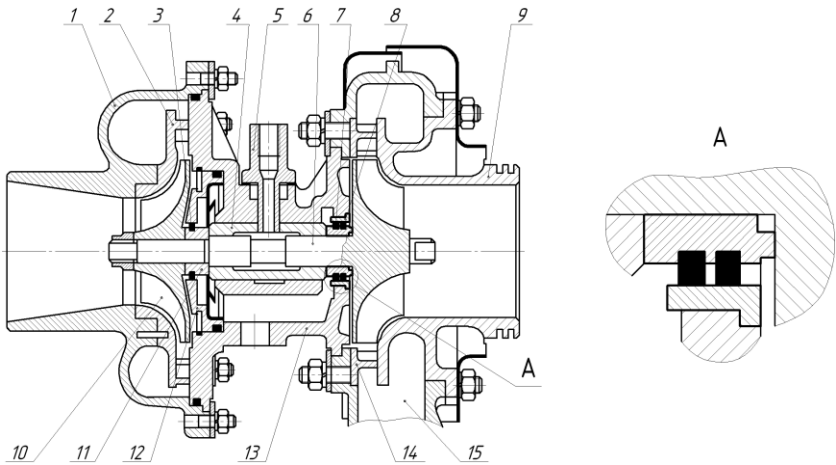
Турбокомпрессор ТКР-11Н-1 в сборе: 1 – корпус компрессора, 2 – вставка компрессора, 3 – кольцо уплотнительное (компрессора), 4 – подшипник, 5 – фиксатор, 6 – вал ротора в сборе, 7 – кольцо уплотнительное (турбины), 8 – втулка, 9 – вставка турбины, 10 – колесо компрессора, 11 – маслоотражатель, 12 – диск уплотнения компрессора в сборе, 13 – корпус средний, 14 – венец соловой в сборе, 15 – корпус турбины.
